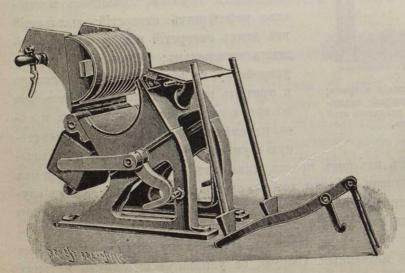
Аппарать для отливки стереотипа съ бумажныхъ матрицъ. Верхняя часть (полуцилиндрическая крышка) поднята— аппаратъ приготовленъ для вкладыванія матрицы.
